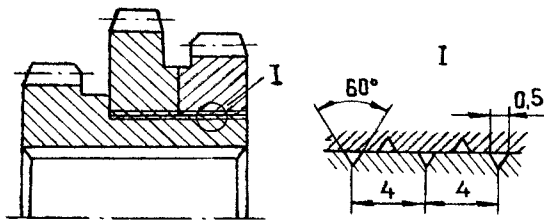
Конструкція клеєного блока зубчастих коліс
